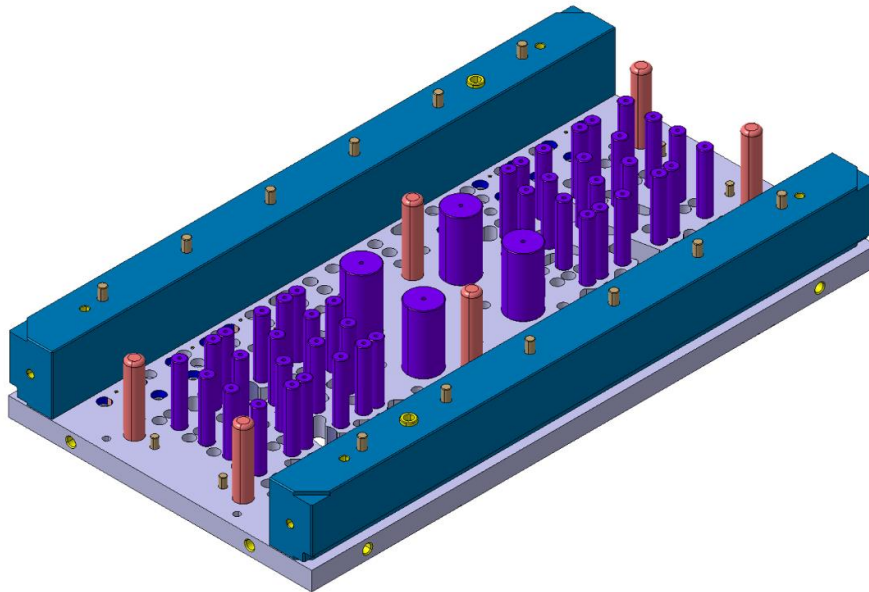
Pilares de suporte a roxo e guias de extrao a rosa
